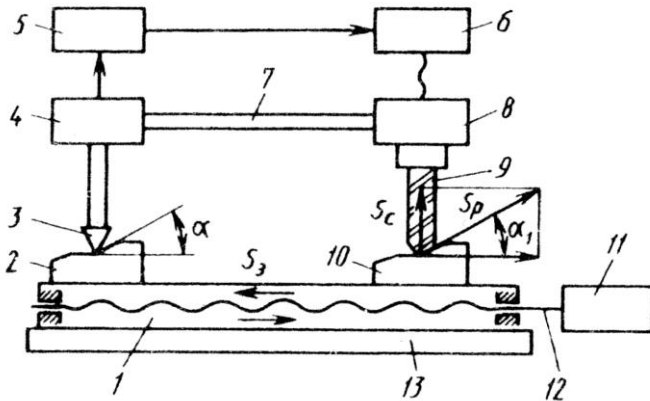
Функціональна схема слідкувальної копіювальної системи вертикально-фрезерного верстата: 1 – стіл вертикально-фрезерного верстата; 2 – копій; 3 – шуп; 4 – копіювальний прилад (головка); 5 – підсилювач; 6 – електродвигун; 7 – жорсткий зворотний зв'язок; 8 – шпиндельна коробка; 9 – фреза; 10 – заготовка; 11 – електродвигун; 12 – ходовий гвинт; 13 – станина;  $S_z$ ,  $S_c$ ,  $S_p$  – відповідно задавальна, слідкувальна та підсумкова подачі
